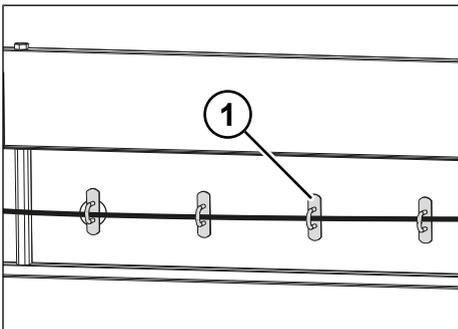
Pattes de fixation de bâche sur la paroi arrière
